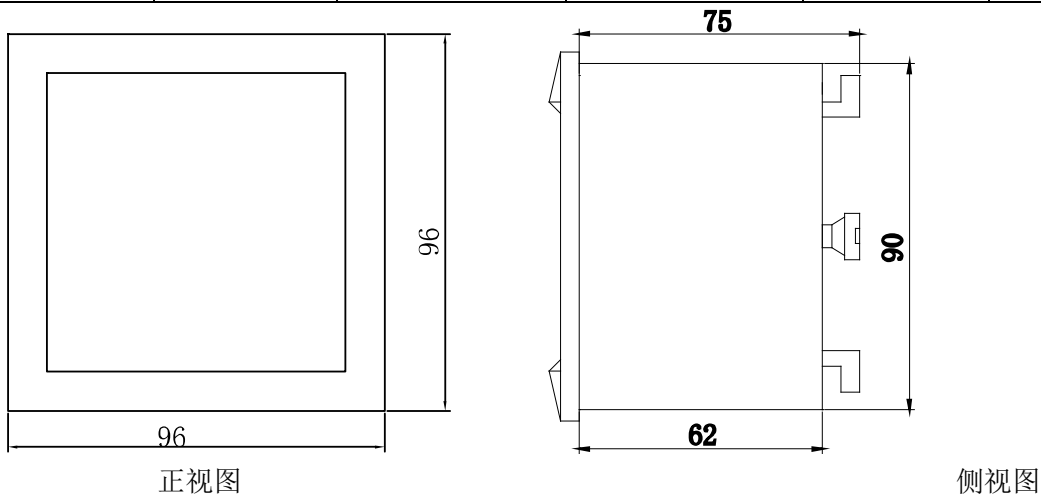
96 型机械尺寸图 (单位: mm)
